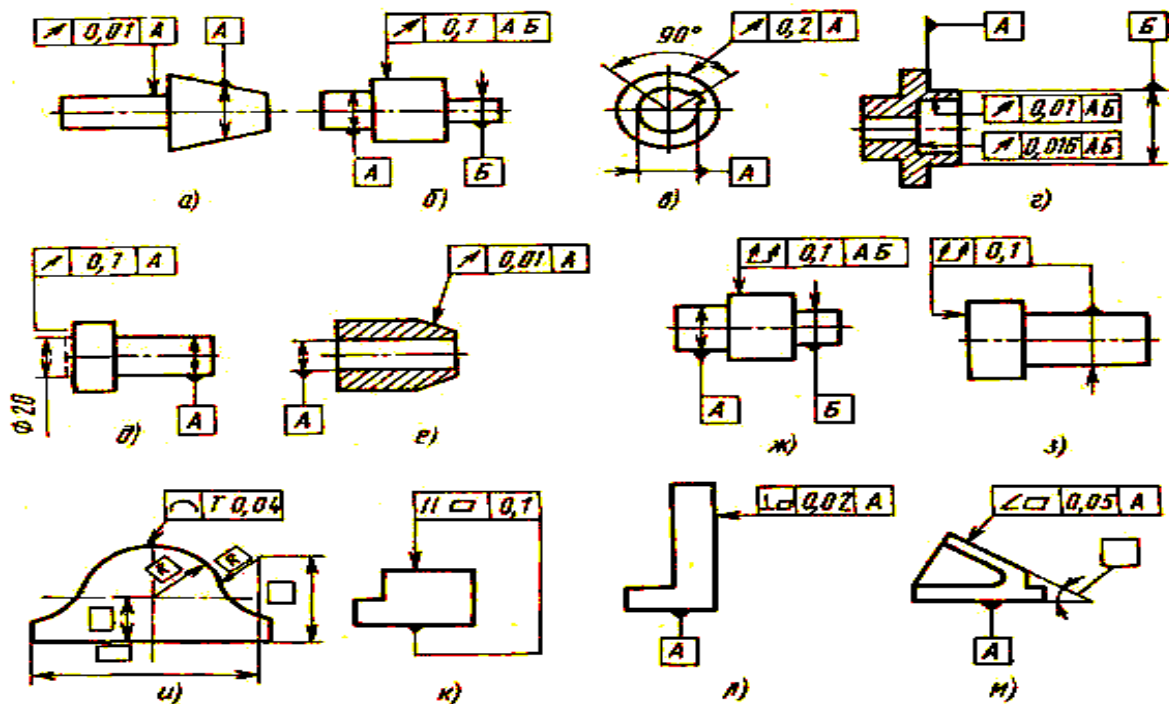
Условные обозначения суммарных допусков формы и расположения поверхностей детали
